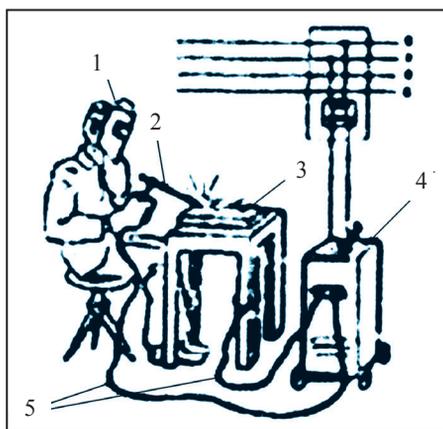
Оборудование для электросварки: 1 – защитная шлем-маска; 2 – электрод; 3 – деталь; 4 – сварочный аппарат; 5 – провода.
